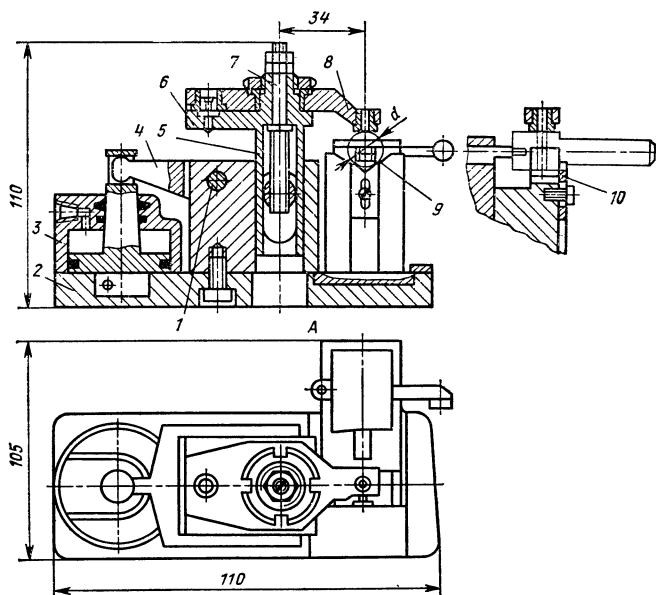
Переналаживаемый кондуктор для сверления контрольных отверстий в головках винтов
